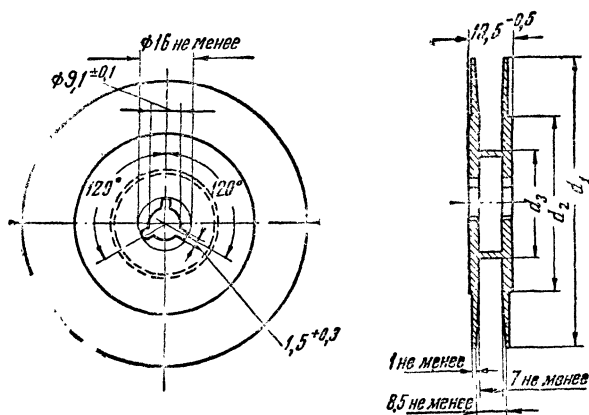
а* — внешний вид сердечника; *б* — кассета для намотки ферромагнитной ленты
